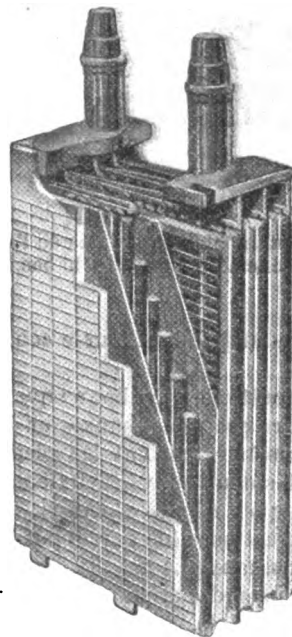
Vue de l'assemblage d'un bloc de plaques de l'accumulateur ironclad.
